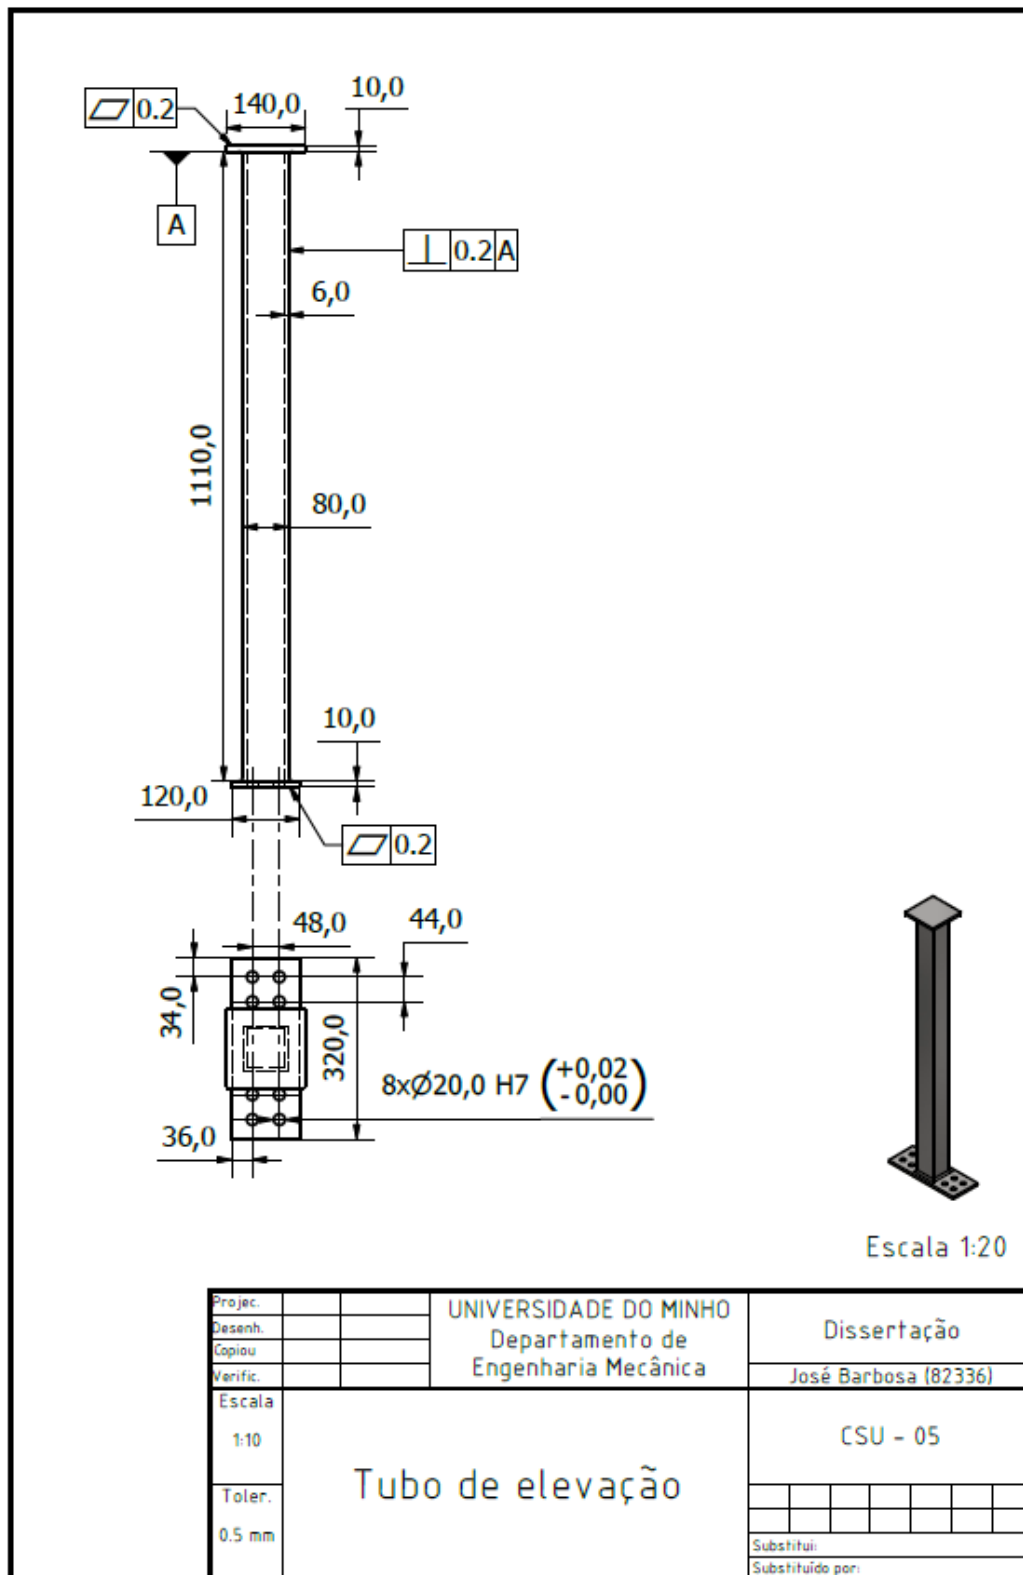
Figura Anexo III-8 – Desenho técnico do tubo de elevação.
